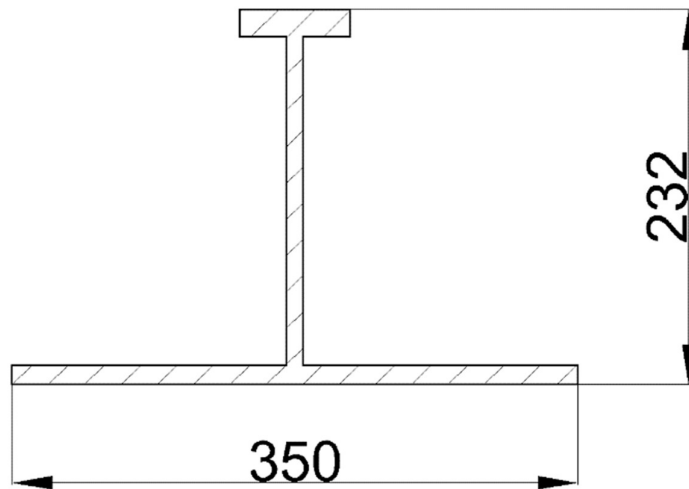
Переріз балки-шпангоута з приєднаним пояском для варіанта конструкції борту з подовженими проміжними шпангоутами і посиленими бортовим стрингером
